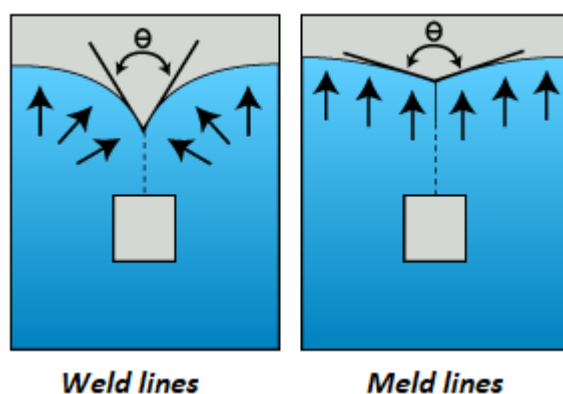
Linhas de Soldadura (adaptado de [28])
